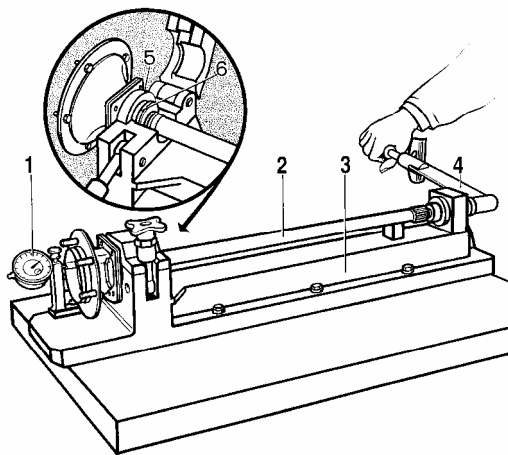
Проверка усилия, с которым выпрессовывается запорное кольцо подшипника полуоси:
